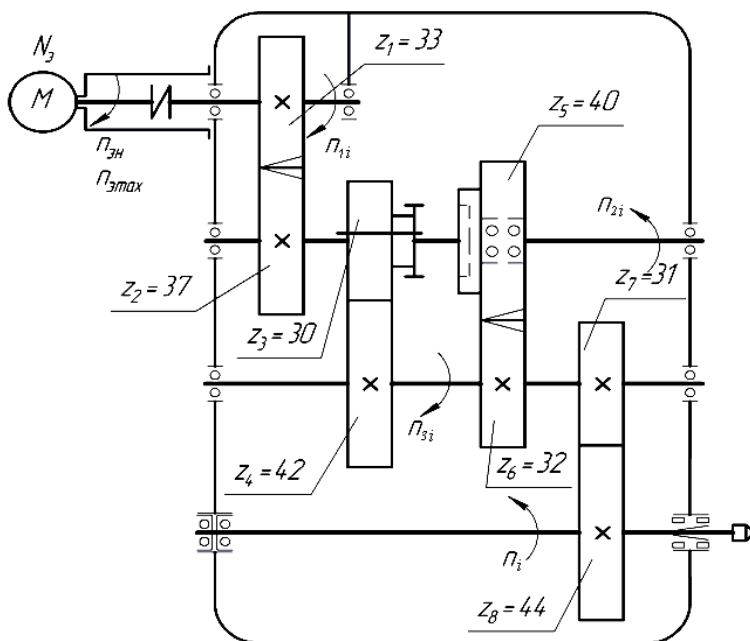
Кинематическая схема главного привода с электромеханическим регулированием электродвигателем и двухступенчатой коробкой скоростей станка с ЧПУ
